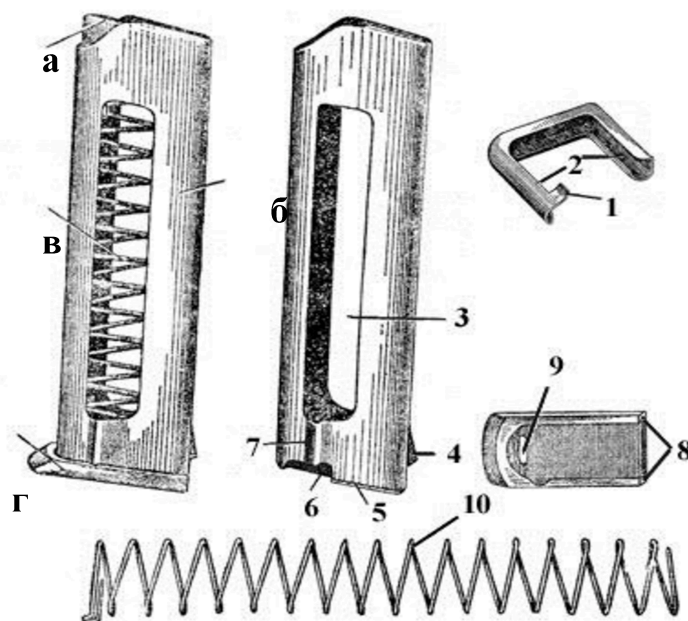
Магазин (а — подаватель; б — корпус магазина; в — пружина подавателя; г — крышка магазина; 1 — зуб; 2 — отогнутые концы; 3 — окно; 4 — выступ; 5 — загнутое ребро; 6 — вырез; 7 — желоб; 8 — пазы; 9 — отверстие; 10 — пружина подавателя)
